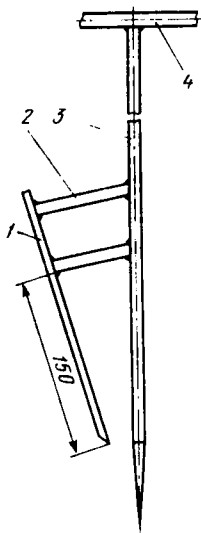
Устройство с плоским ножом для удаления корневищ из почвы: 1 — нож; 2 — консоль; 3 — стержень; 4 — рукоятка
